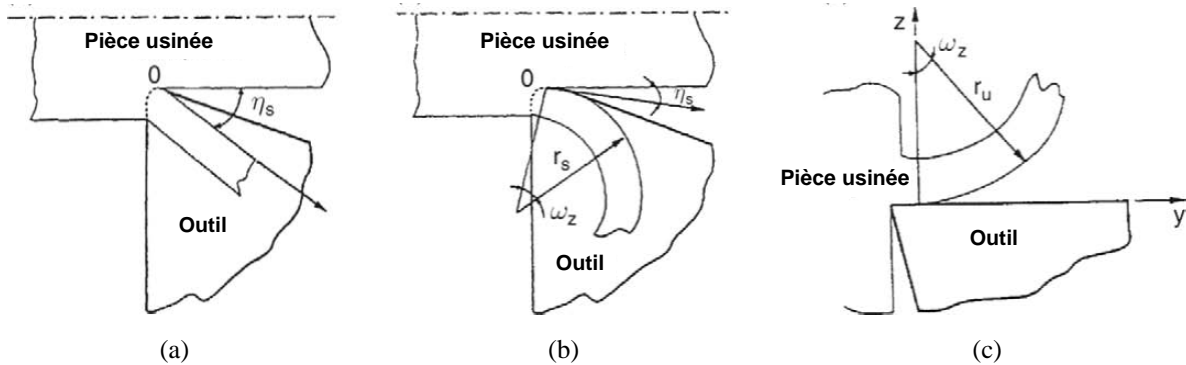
Trois formes basiques de copeau : (a) copeau droit, (b) copeau courbé dans le plan de la face de coupe, (c) copeau courbé dans le plan orthogonal à la face de coupe, [JAW\_93]
